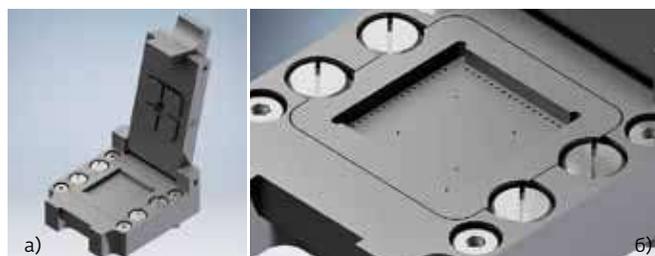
КУ для безвыводных корпусов (со скрытием контактов): а – общий вид; б – увеличенный вид
